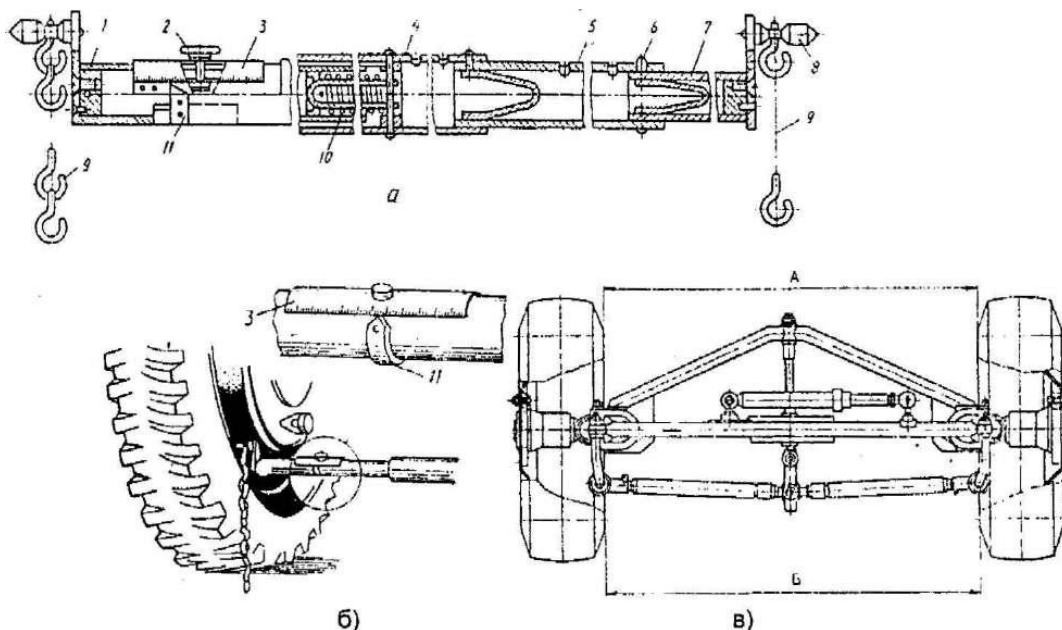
Проверка сходимости передних колес машин: а - линейка КИ-650; б - установка линейки; в - замер сходимости колес; 1 - подвижная труба; 2 - винт; 3 - шкала; 4 - наружная труба; 5 - промежуточная труба; 6 - фиксатор; 7 - удлинитель; 8 - контактный наконечник; 9 - цепочка; 10 - пружина; 11 - стрелка; I - места замера сходимости колес: А - расстояние между задней частью колес; Б - расстояние между передней частью колес
